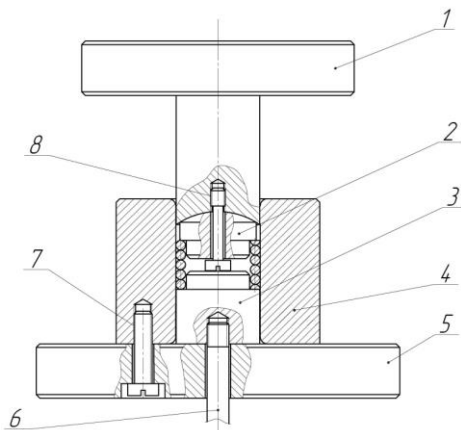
Схема устройства для упрочнения внутренней пружины клапана двигателя автомобилей ВАЗ
